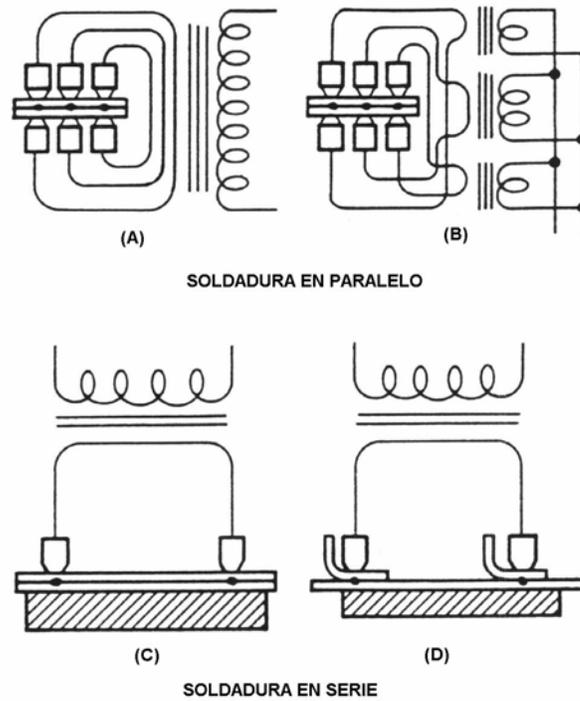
Arreglo Típico para Soldadura por Puntos Múltiple
